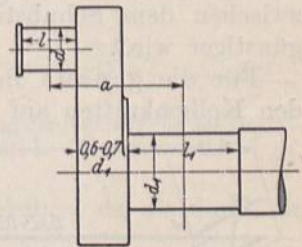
Skizze der Stirnkurbel zur Maschine
